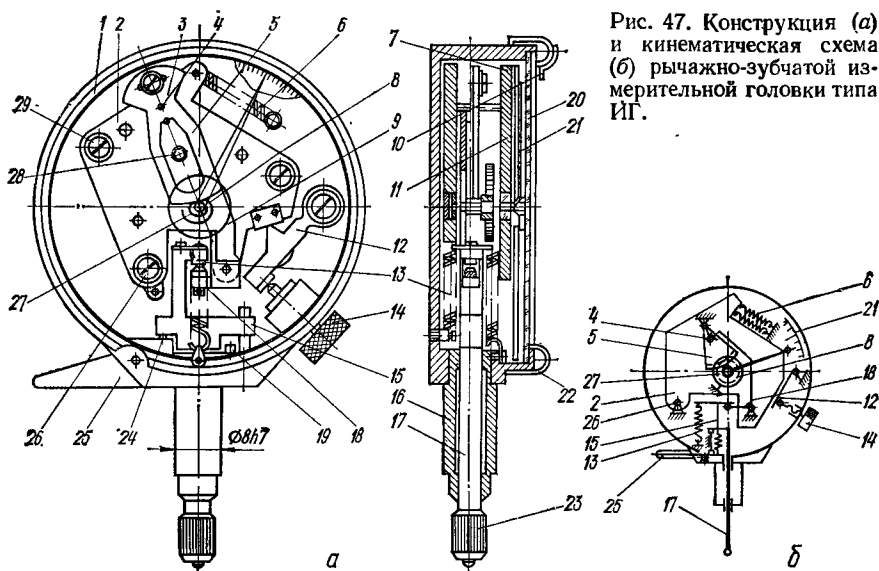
Конструкция (а) и кинематическая схема (б) рычажно-зубчатой измерительной головки типа ИГ.
